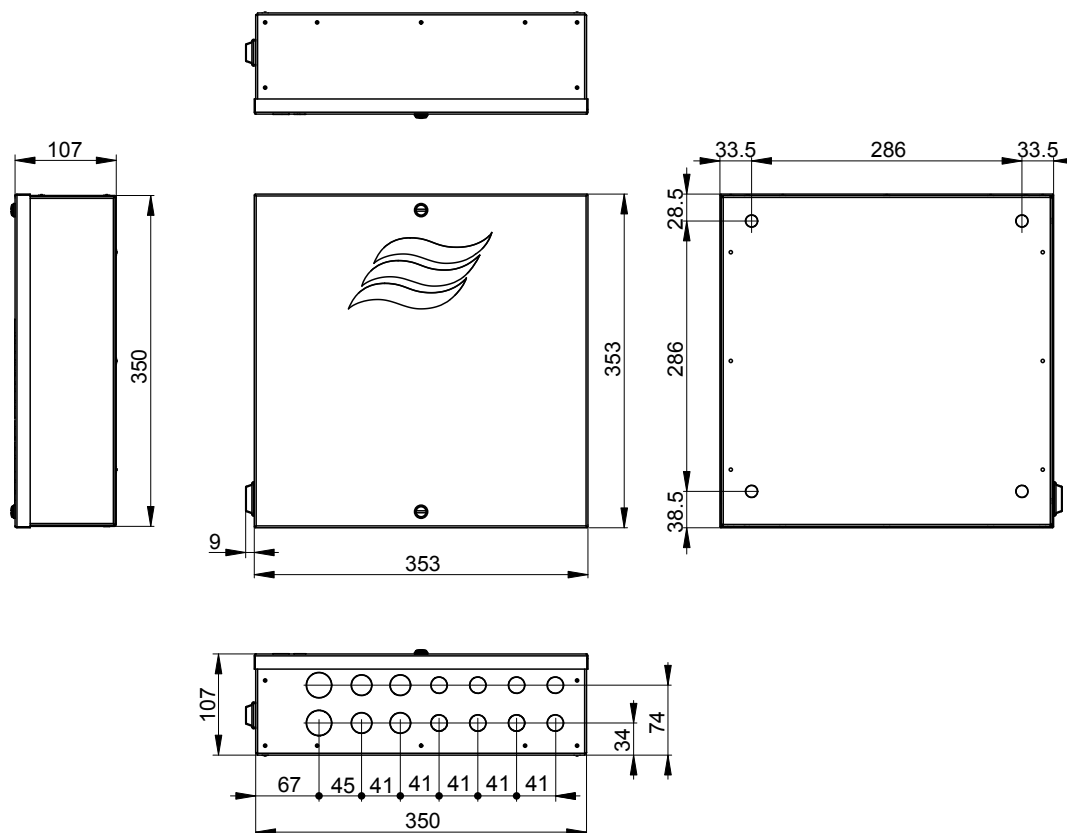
Dessin coté du Condair Delta SPA Control Box (dimensions en mm)
